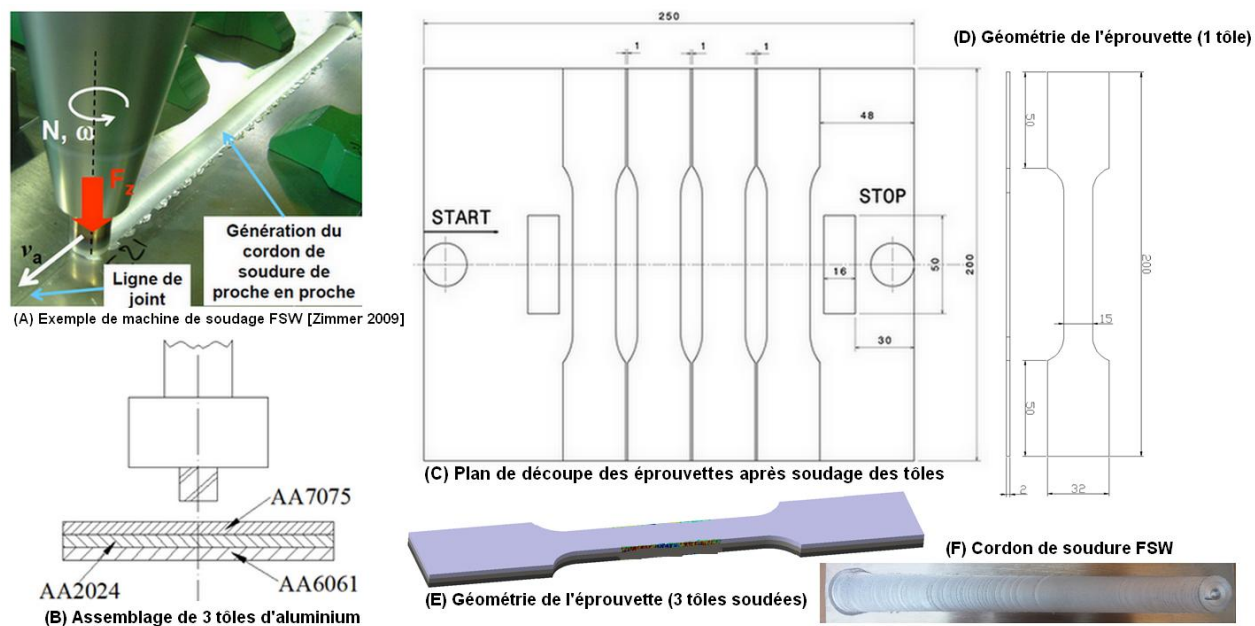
Protocole de soudage par FSW des tôles d'aluminium et usinage des éprouvettes
